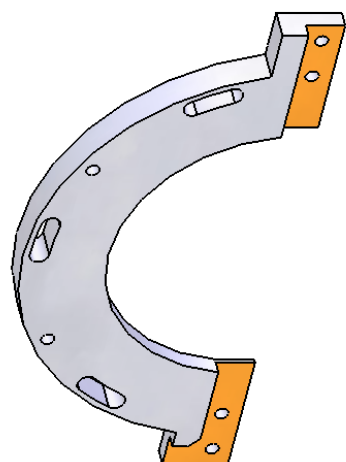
Ubicación de la brida de apoyo y, al centro, el obturador.
